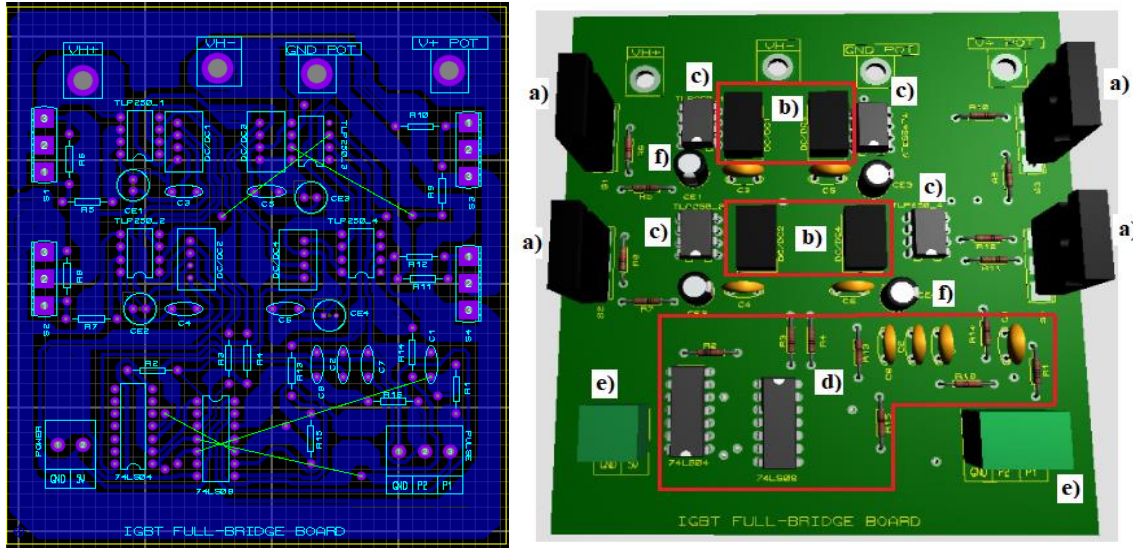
1.- Diseño del esquemático del PCB del puente H, a-) Routing del PCB del puente H, b-) PCB en 3D puente H.
